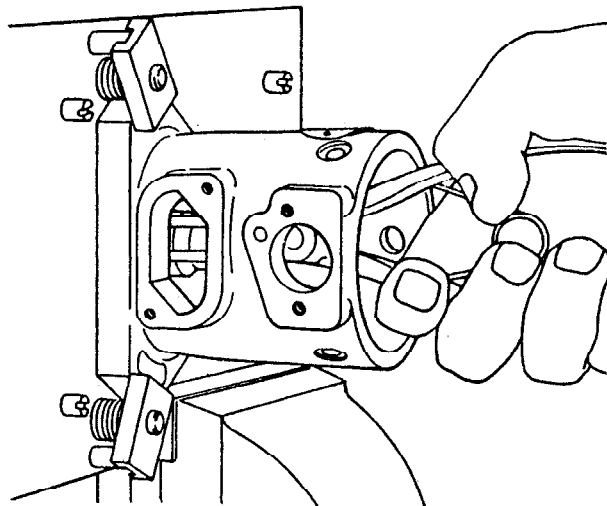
Para sacar la cabeza hidráulica y rotor A) de la cubierta B) de la bomba
